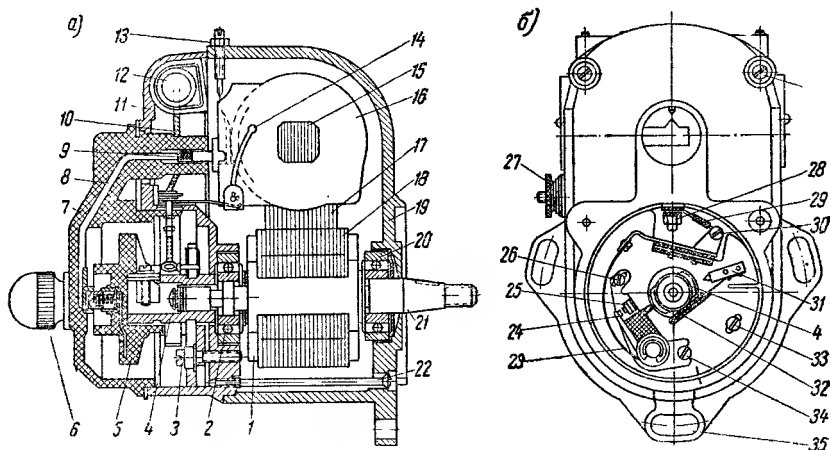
Конструкция магнето М-47Б: а — продольный разрез; б — вид со стороны прерывателя
